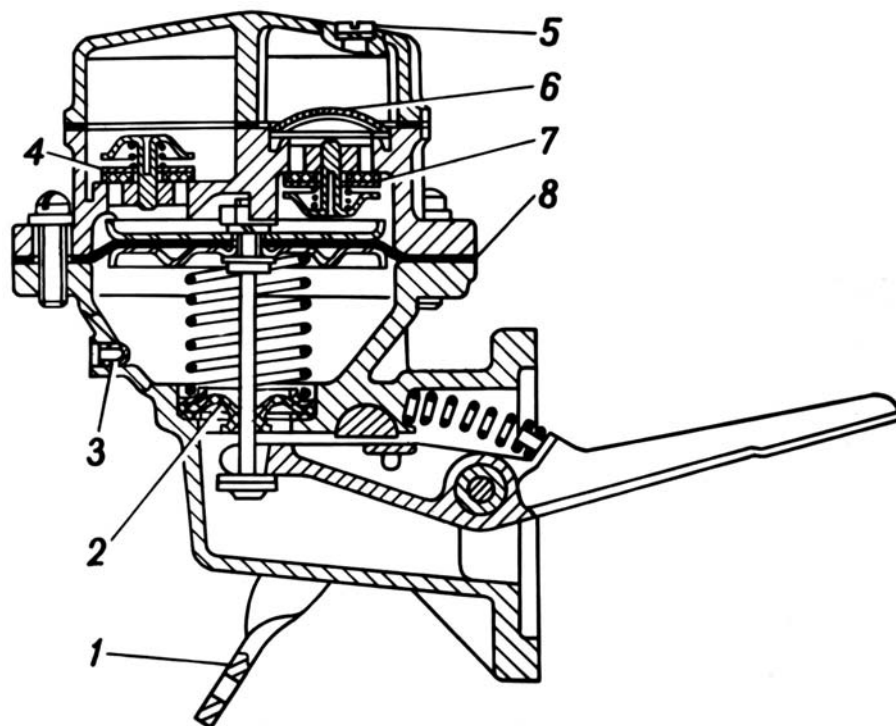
Топливный насос: 1 - рычаг ручного привода; 2 - уплотнитель; 3 - сетчатый фильтр контрольного отверстия; 4 - нагнетательный клапан; 5 - винт крепления крышки фильтра; 6 - сетчатый фильтр; 7 - всасывающий клапан; 8 - диафрагма
